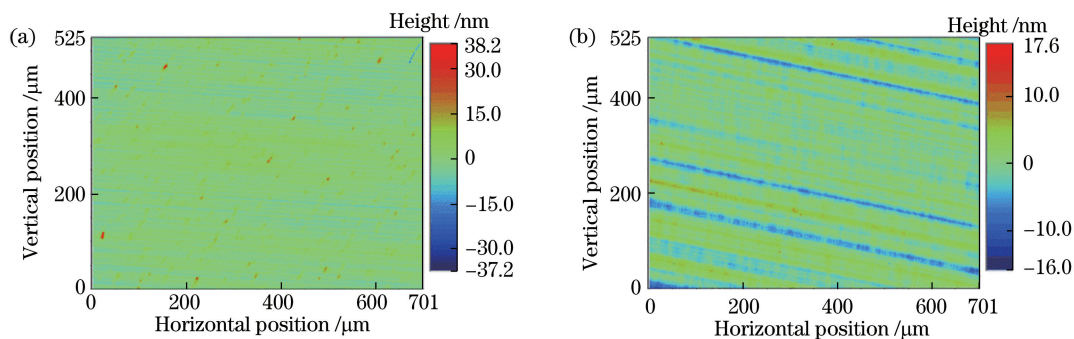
不同结构刀具加工得到的 KDP 晶体表面形貌。(a) 圆弧刃刀具;(b) 结构优化刀具
